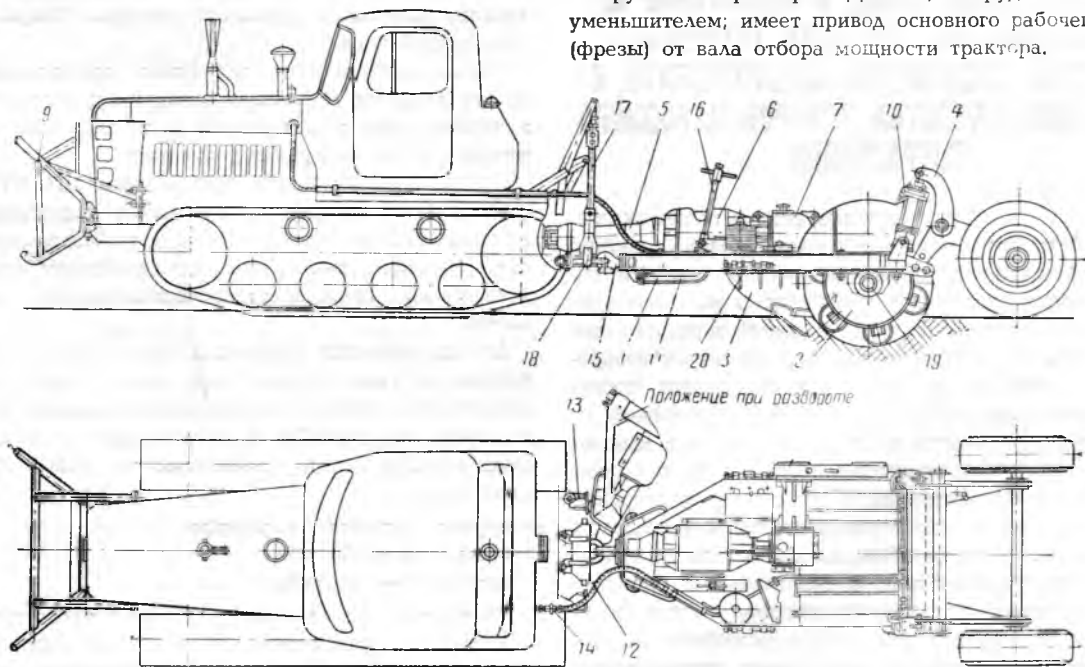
Общая схема фрезерной машины МФ-0,9:
